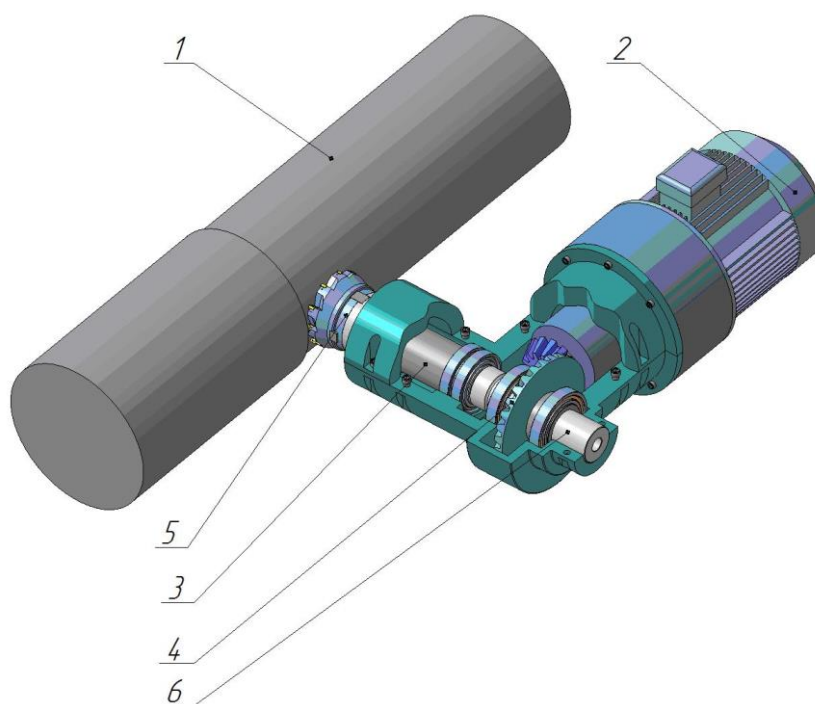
Общий вид установки для фрезоточения крупногабаритных деталей типа «Вал»
